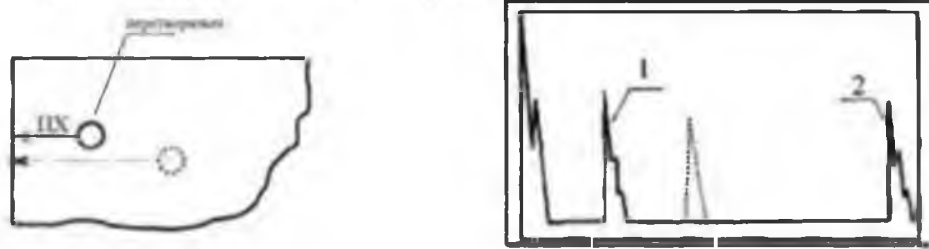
Кутове зварне з'єднання з дефектом
